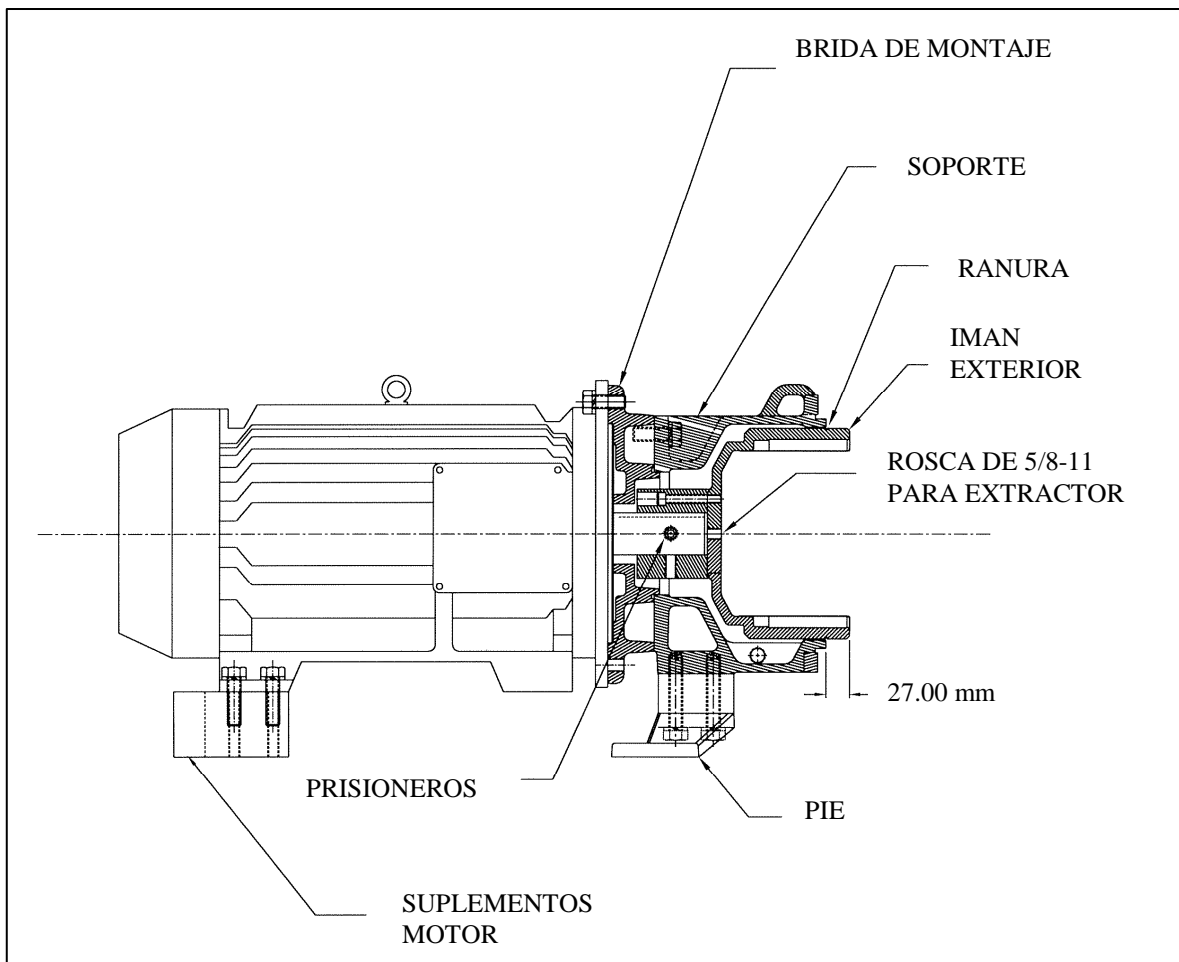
CONJUNTO MOTOR PARA MOTORES IEC
